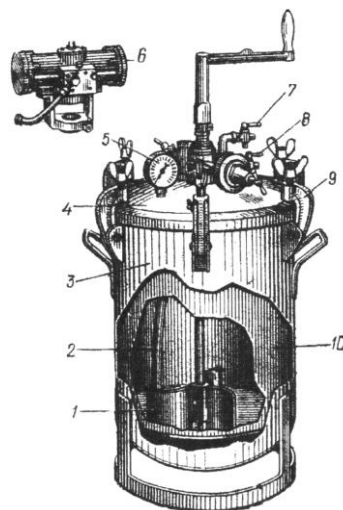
Лаконагнітальний бак: 1 - мішалка; 2 - трубка для лаку; 3 - бак; 4 - кришка; 5 - манометр; 6 - редуктор; 7 - кран для повітря; 8 - кран для подавання лаку з бачка; 9 - гвинти; 10 - бачок для лаку
